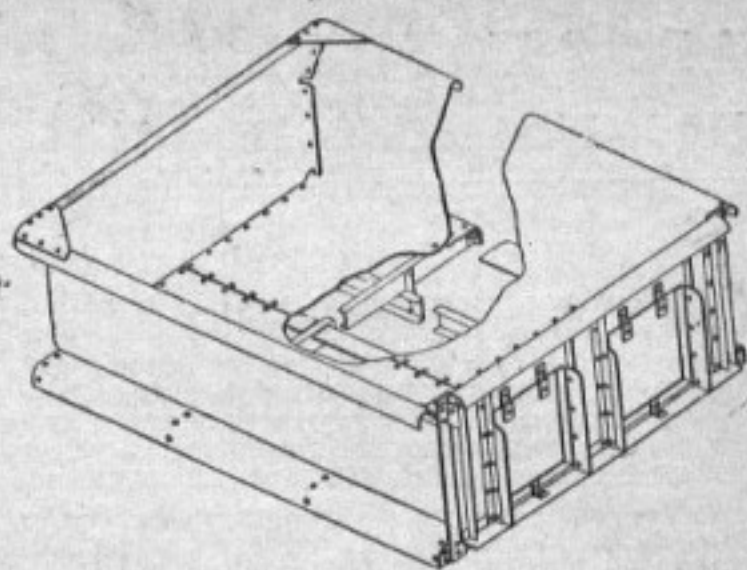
Алюминиевый опрокидывающийся кузов для перевозки угля
